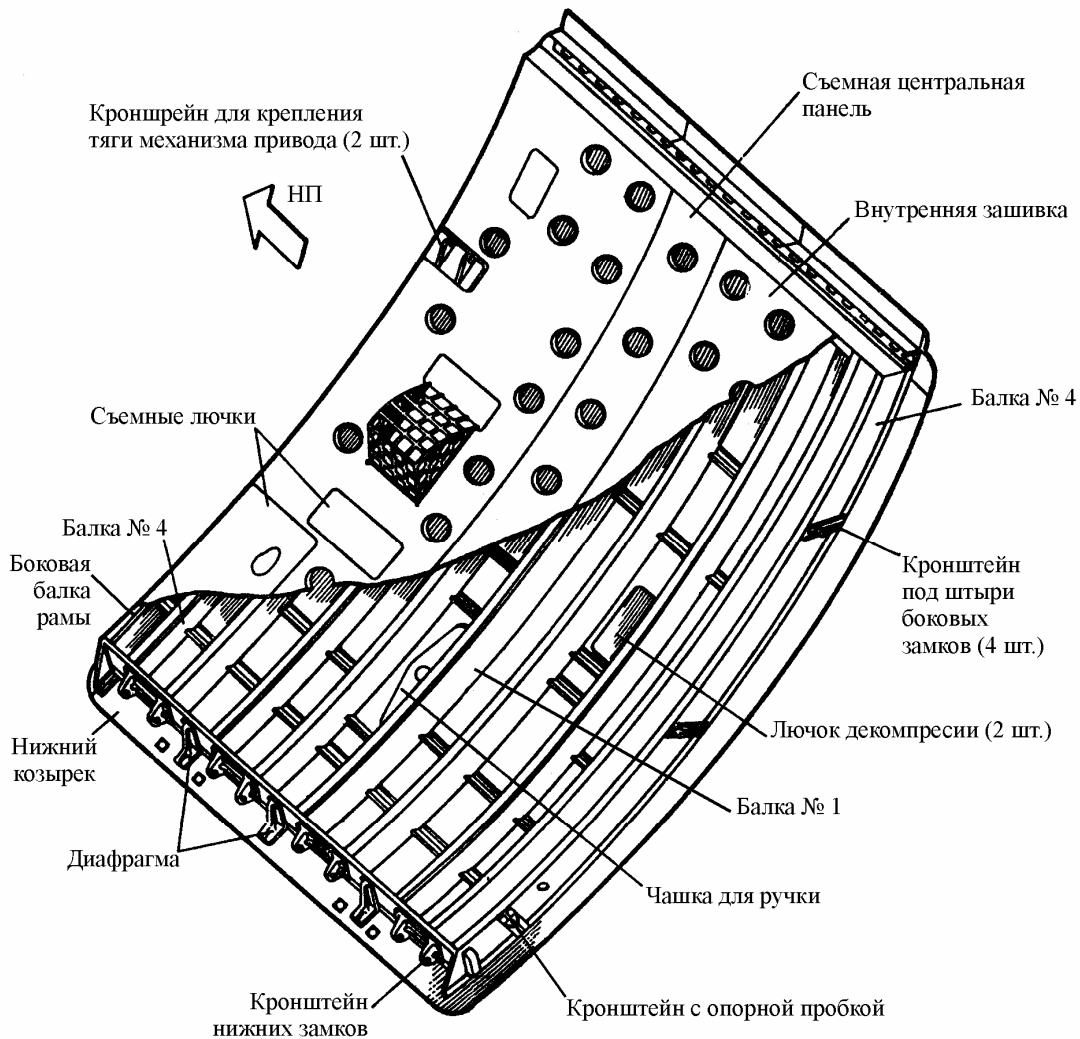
Крышка грузовой двери (вид изнутри фюзеляжа)
